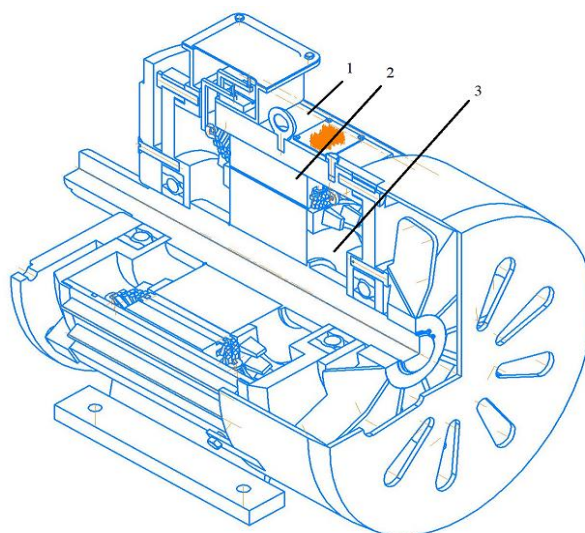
Асинхронный двигатель с короткозамкнутым ротором с вырезом одной четверти (1 – корпус, 2 – статор, 3 – ротор)
